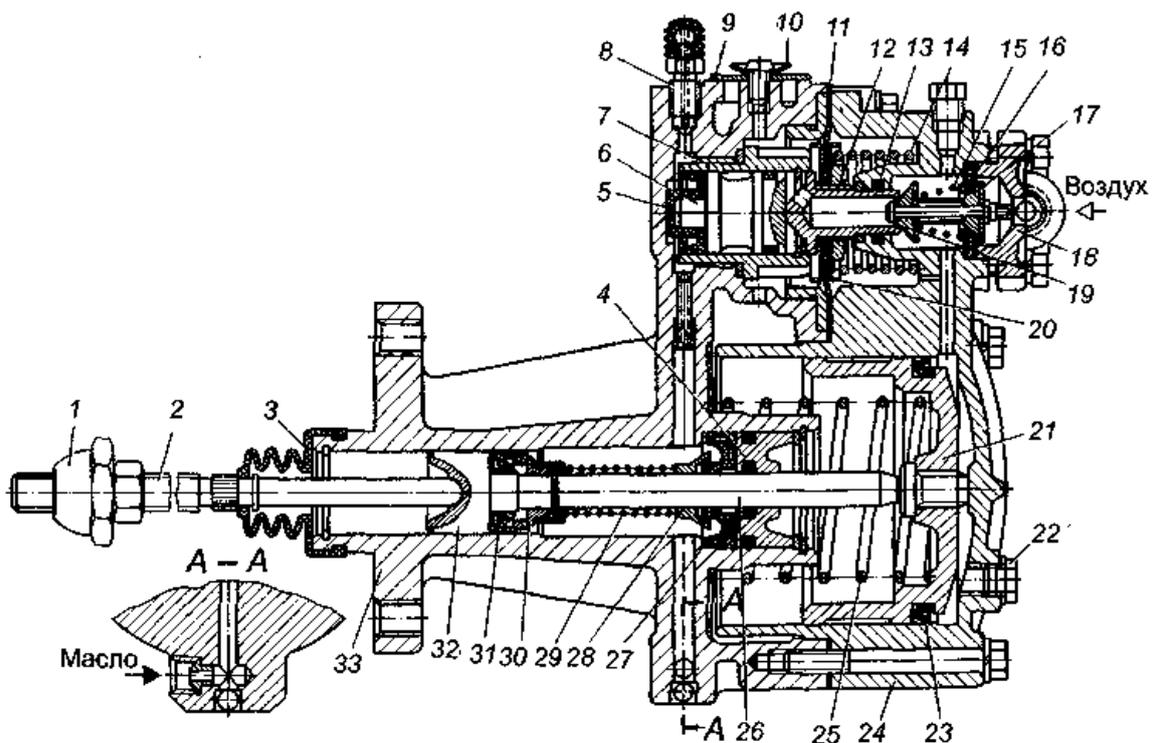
Пневмогидроусилитель привода сцепления автомобилей марки «КамАЗ»:
